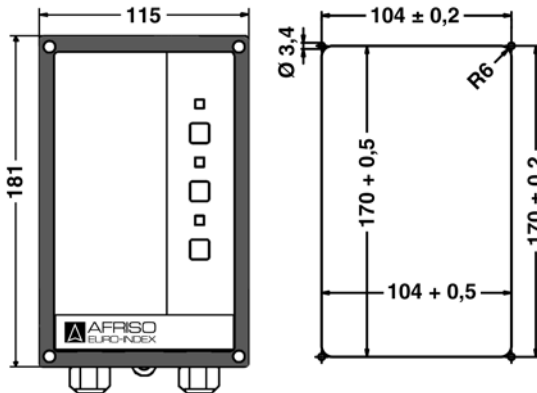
Messumformer mit Montagerahmen für den Einbau in Schalttafeln; rechts: Schalttafel Ausschnitt
